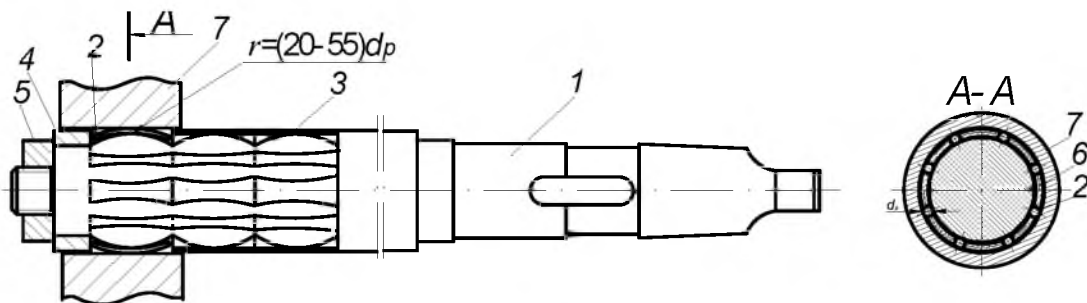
Пристрій для розкатування нежорстких втулок гнучкими роликами
